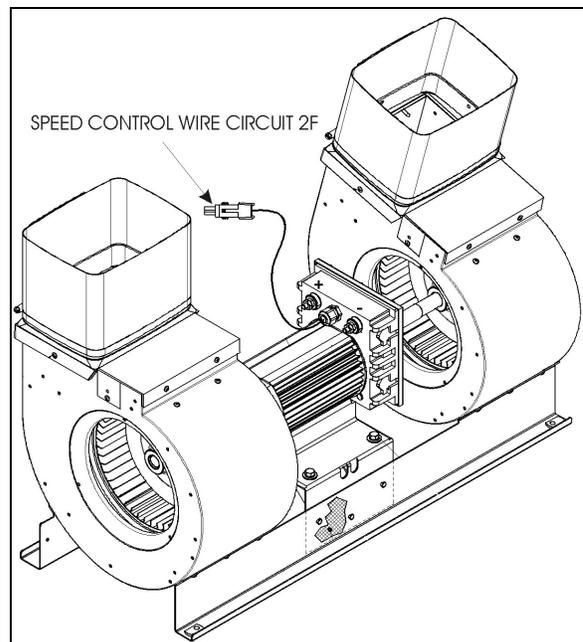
ENSAMBLE DE MOTOR DEL EVAPORADOR
